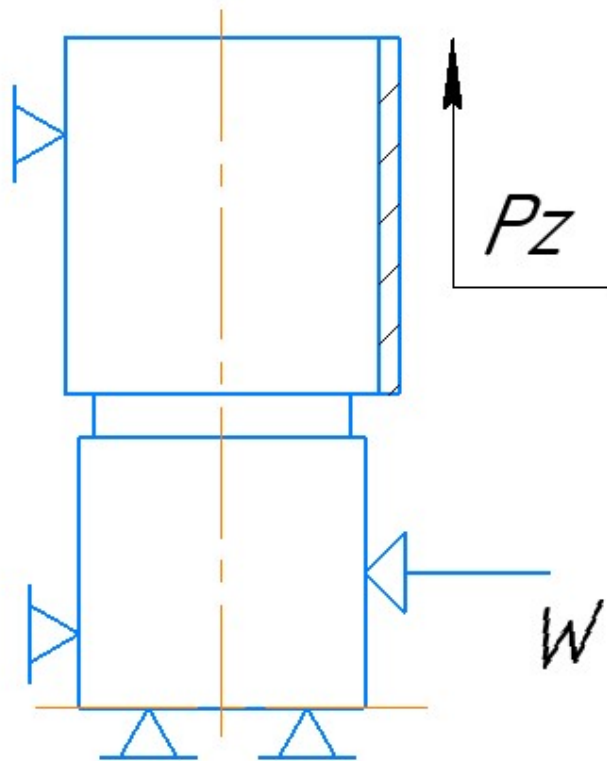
Схема для розрахунку сили закріплення  $W$  при фрезеруванні
